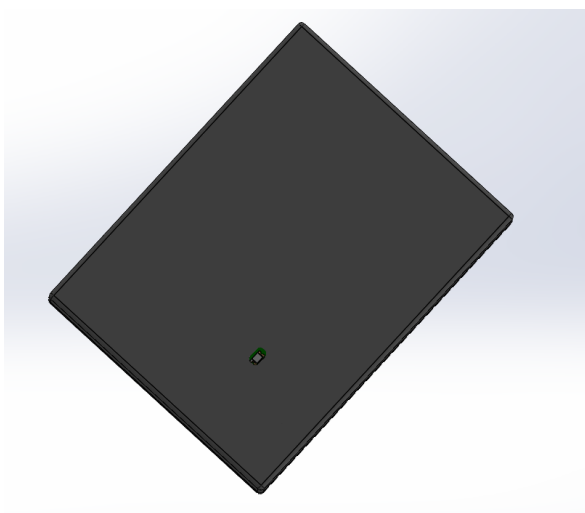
Загальний вигляд корпусу пристрою знизу
